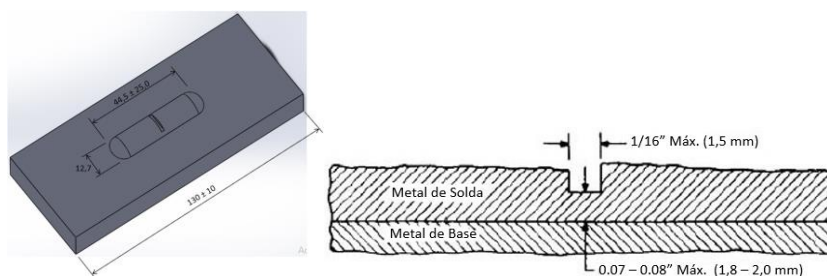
Corpo de prova DWT, soldado e vista em corte longitudinal do entalhe (ASTM E208-17).
